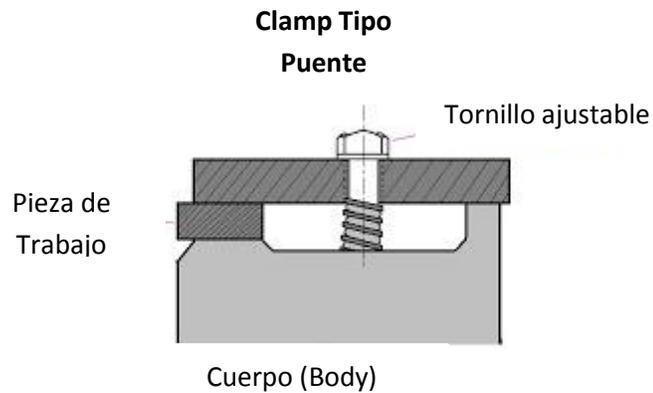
Clamp Tipo Puente. Fuente: American Machinist
